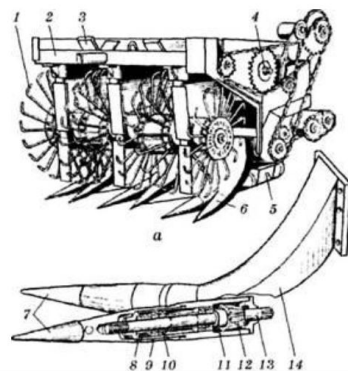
Активна вилка: а – викопувальний пристрій в зборі
